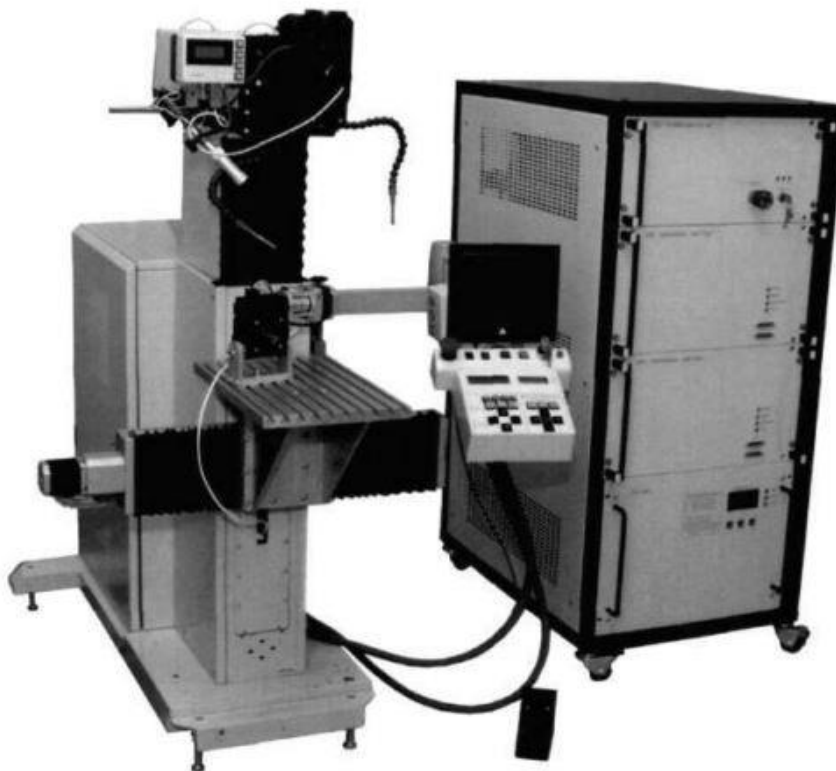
Аппарат для лазерной сварки ЛТА 4-2
